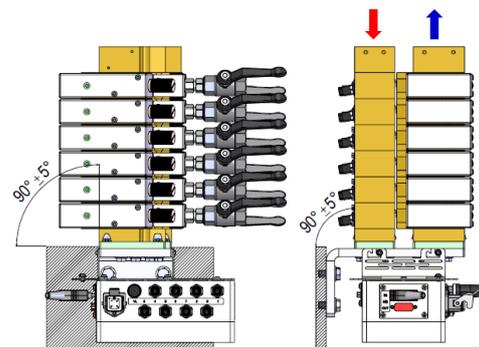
Einbaulage vertikal Bsp. Ausführung links
